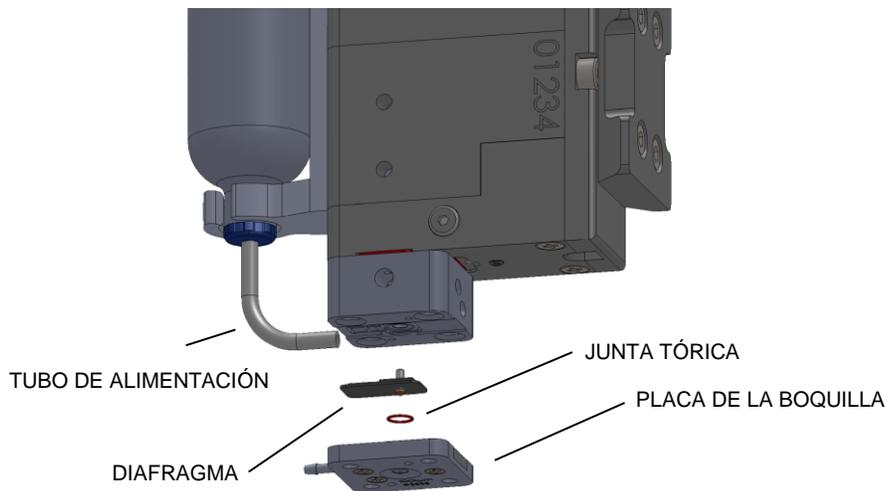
Bloque del calentador de HV-9500, diafragma, junta tórica y placa de boquilla
